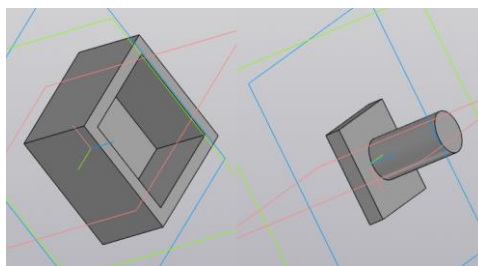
Ячейка для образца почвы и прессик для создания ровной поверхности
